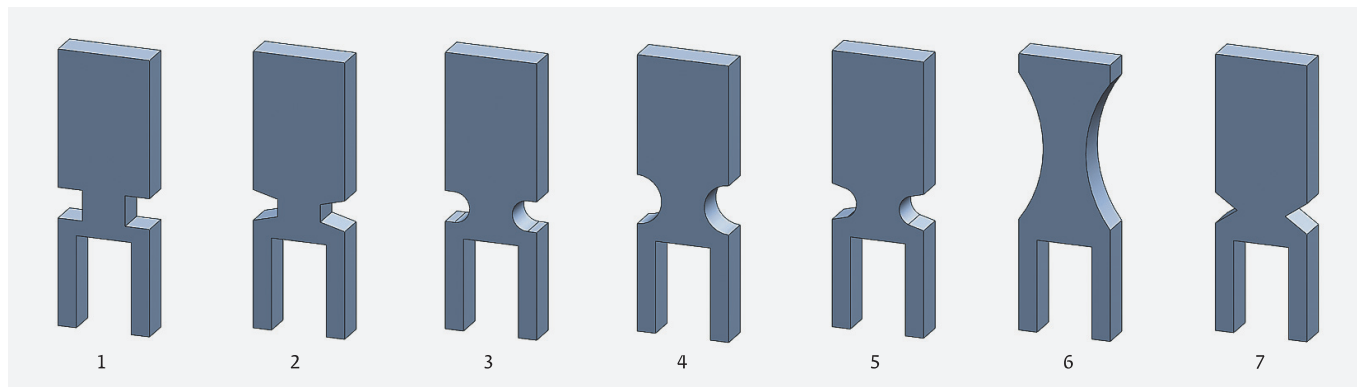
Типы форм концентраторов напряжений в области перемычки резонатора: 1 – квадратная форма концентратора, 2 – трапецевидная форма, 3 – U-образная форма, 4 – цилиндрическая форма, 5 – V-образная форма с цилиндрической поверхностью у вершины, 6 – цилиндрическая форма с большим радиусом закругления, 7 – V-образная форма
